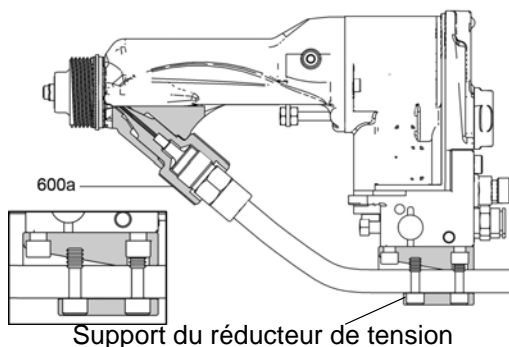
Raccordez le flexible pour fluide à base aqueuse
